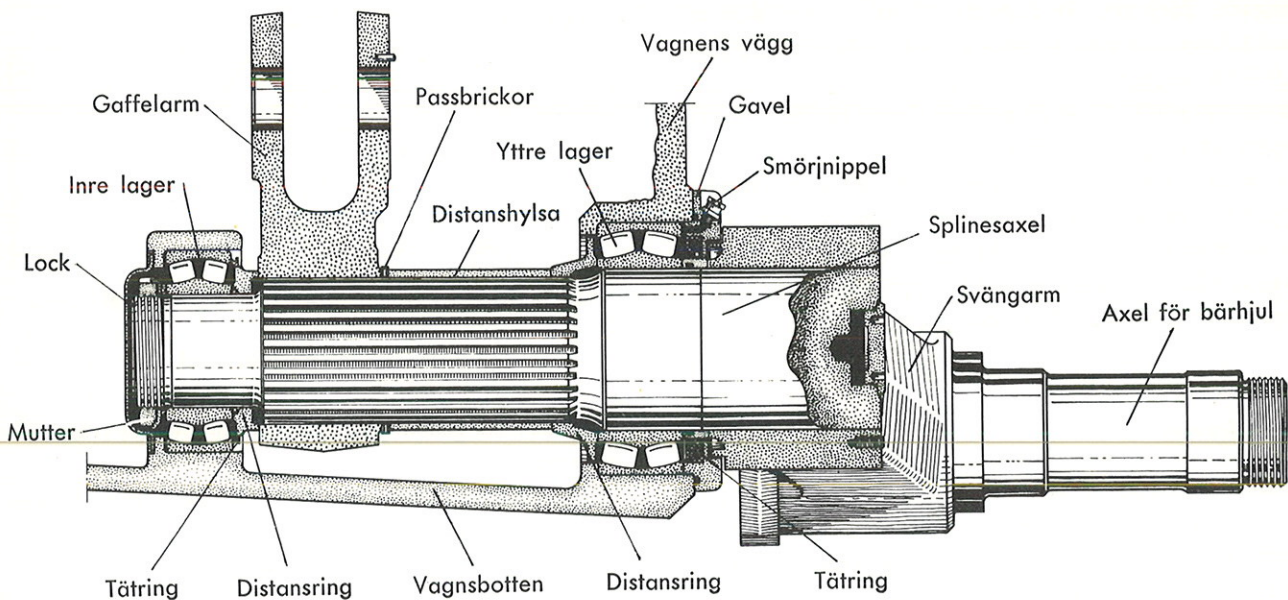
Pendelarmarnas lagring (mellanbärhjul)
